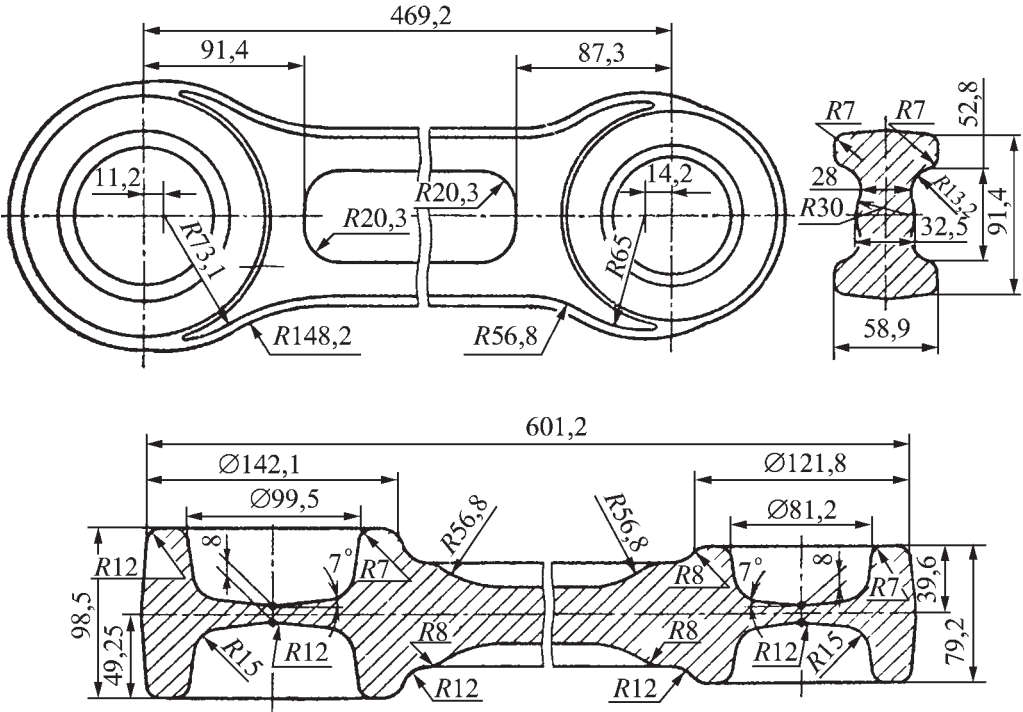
Типовой чертеж поковки для изготовления штампа (горячей поковки)
